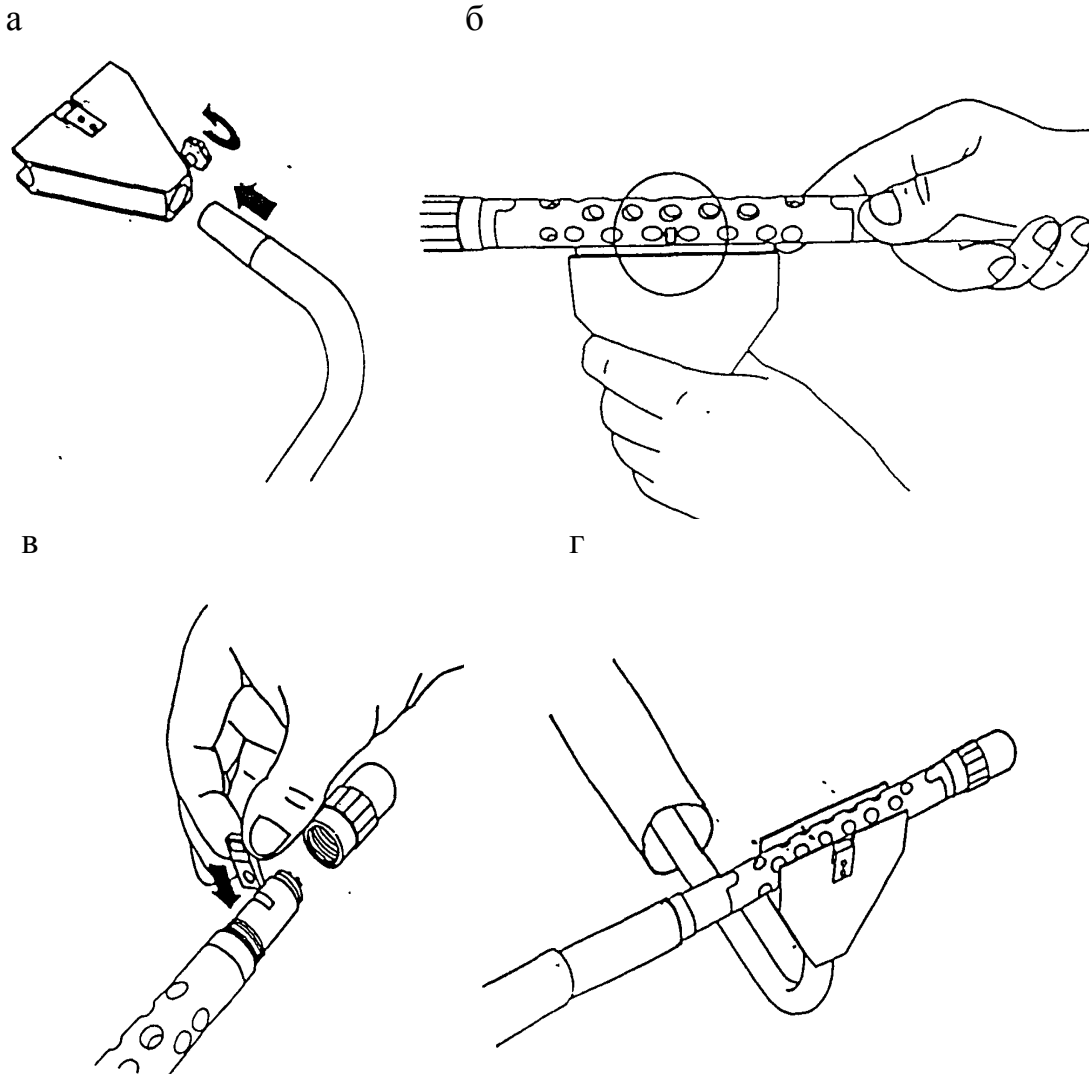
Последовательность сборки и установки пробозаборного устройства
